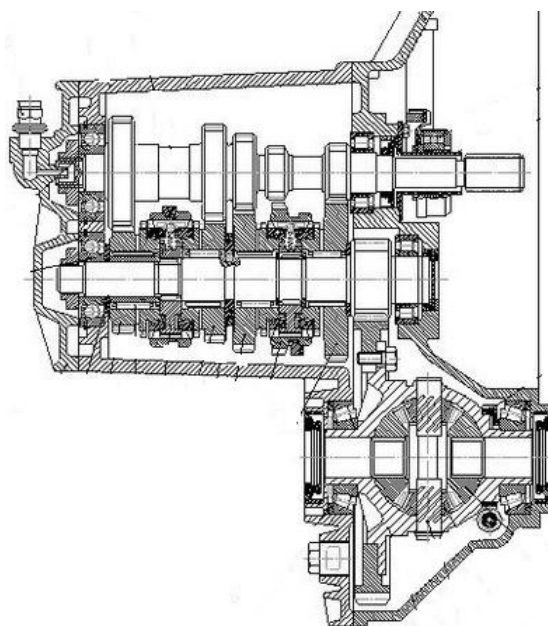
Конструкция четырехступенчатой КПП ВАЗ-2108
